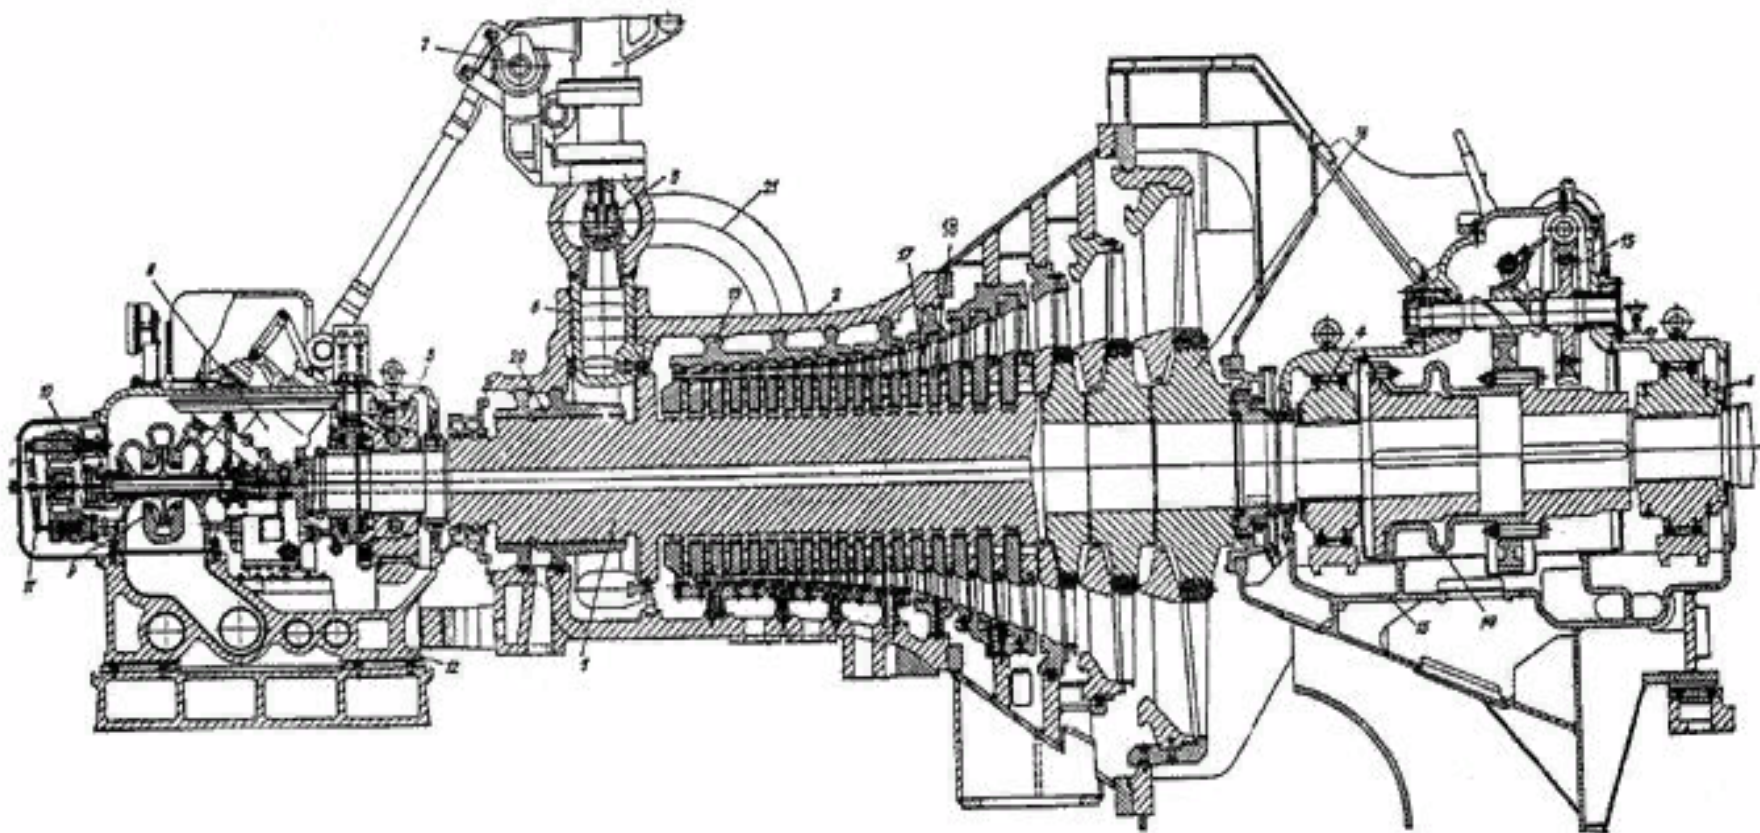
Продольный разрез турбины К-50-90: 1 – ротор турбины; 2 – корпус турбины; 3 – опорно-упорный подшипник; 4 – опорный подшипник; 5 – регулирующий лапан; 6 – сопловая коробка; 7 – кулачковый вал; 8 – сервомотор; 9 – главный масляный насос; 10 – регулятор скорости; 11 – следящий золотник; 12 – картер переднего подшипника; 13 – валоповоротное устройство; 14 – соединительная муфта; 15 – выхлопной патрубок турбины; 16 – насадные диски; 17 – рабочие лопатки; 18 – диафрагмы; 19 – обоймы диафрагм; 20 – обоймы концевое уплотнения; 21 – перепускная труба (от стопорного к регулиющему клапану).
